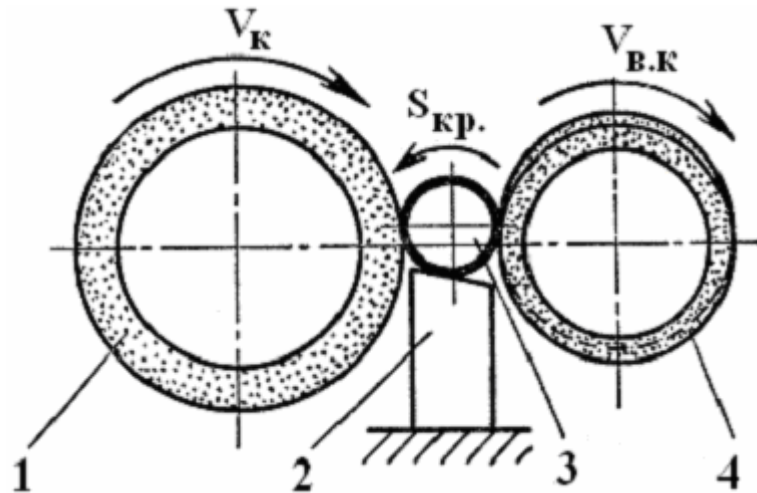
Схема обработки заготовки на бесцентрово-шлифовальных станках:
